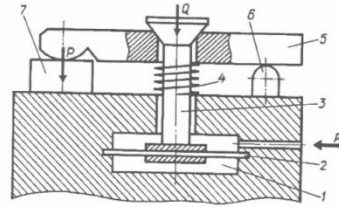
Схема прихоплювача (важіль другого роду), що діє від діафрагменого пневмопривода: 1 – камера; 2 – гумова діафрагма; 3 – шток; 4 – пружина; 5 – прихоплювач; 6 – опора; 7 – заготовка
